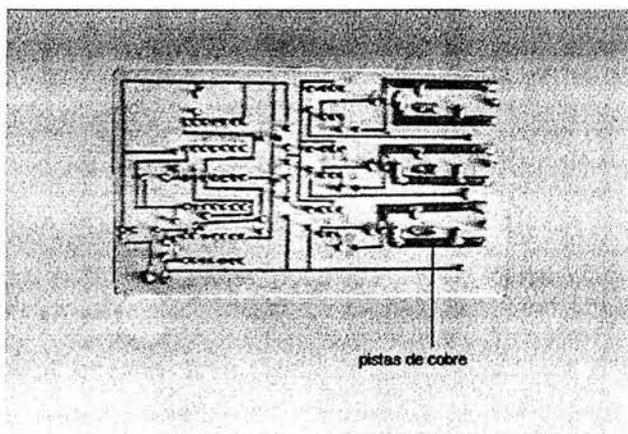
Construcción de pistas en una tablilla de cobre y montaje de los componentes.
